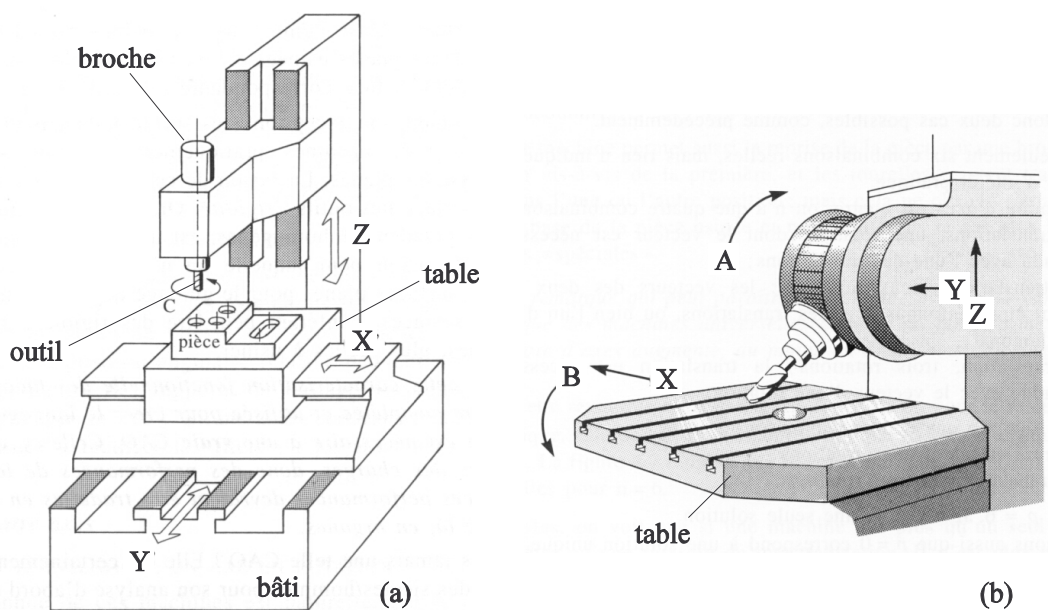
éléments d'une machine-outil (a) et définition des axes d'une machine 5-axes (b) [pru93a]
